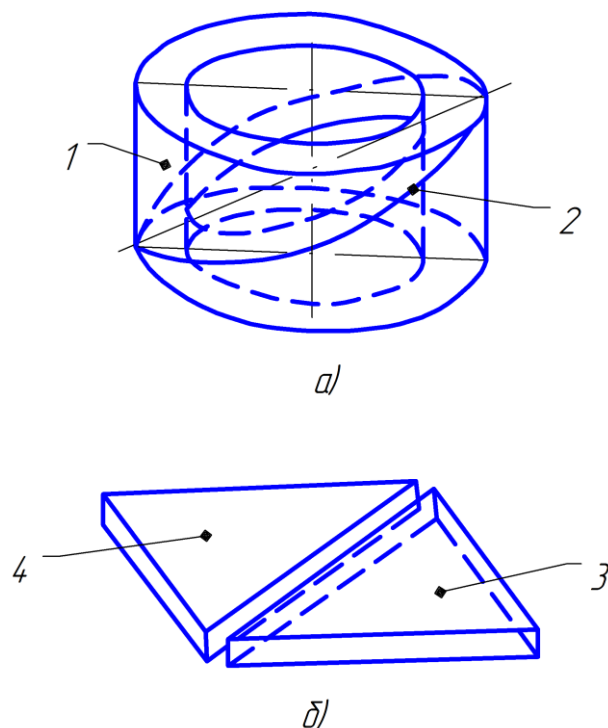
Абразивный круг 1 с линией развертки 2 (а), вырубаемая заготовка (б)
